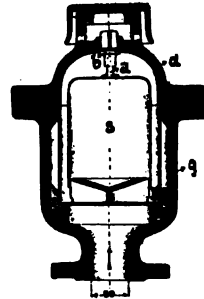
Luftventil mit Schwimmer. (Reuther.)
